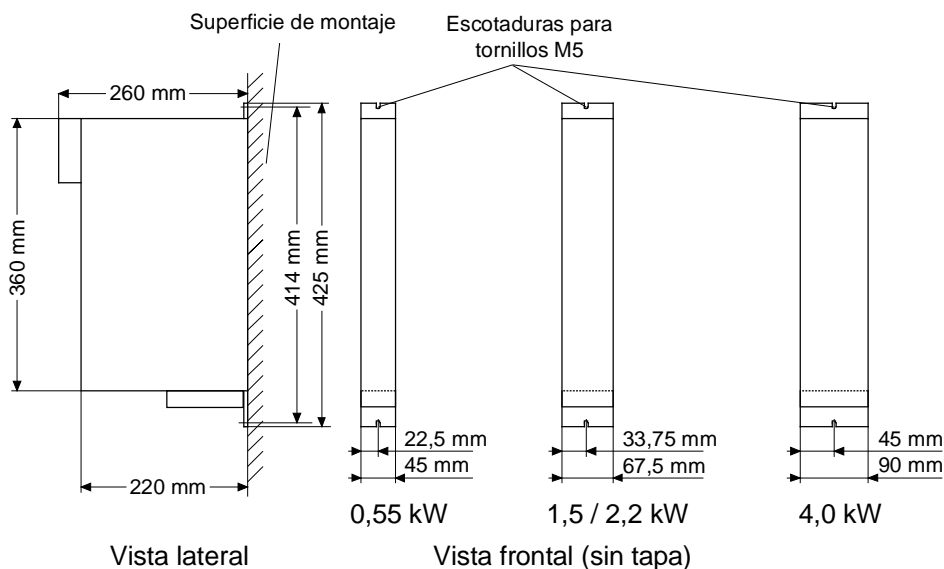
Croquis acotado para equipos con una anchura de hasta 90 mm
